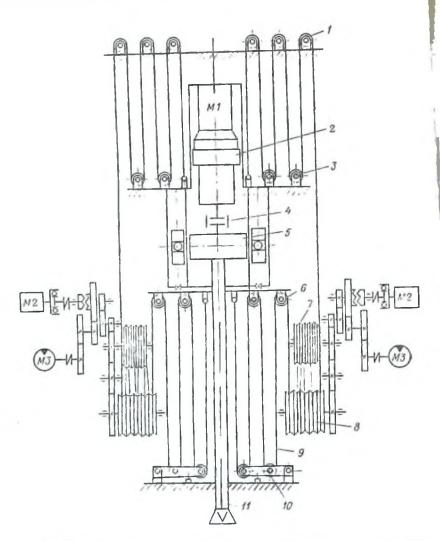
Кинематическая схема вращательно-подающего механизма с канатнополиспастной системой подачи станка шарошечного бурения СБШ-320-36
